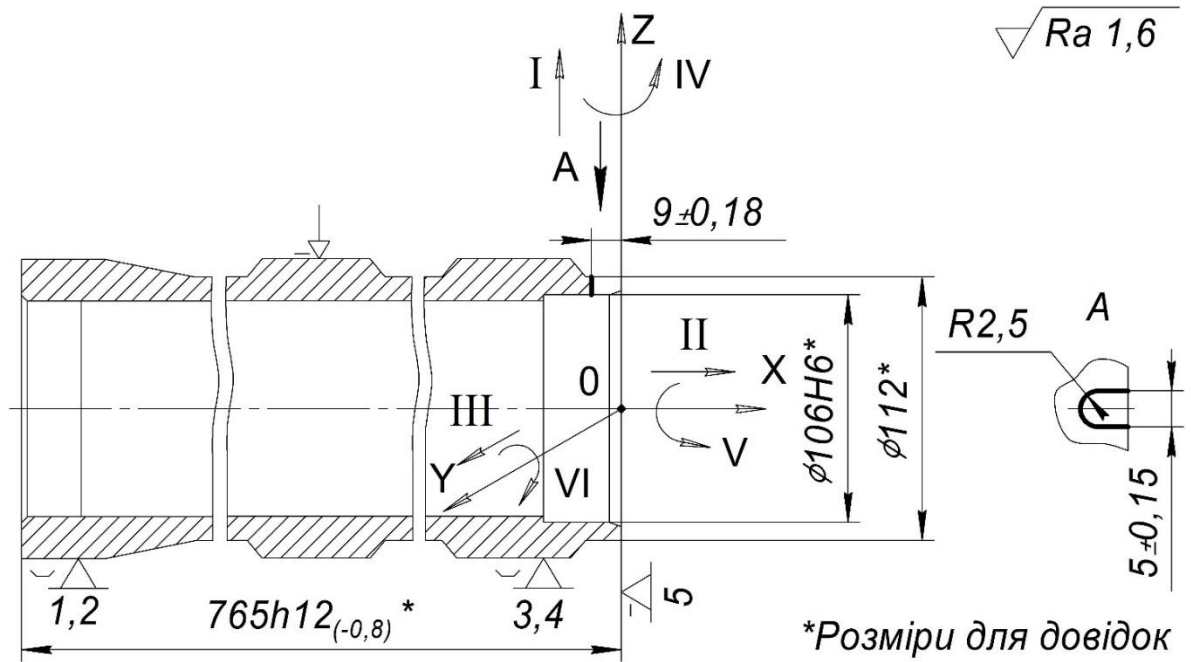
Схема базування заготовки на операції 040 «Фрезерна з ЧПК»
